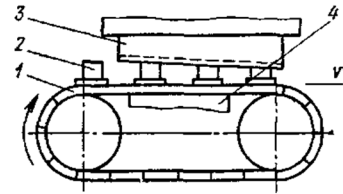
Схема обработки заготовок на протяжном станке непрерывной обработки
